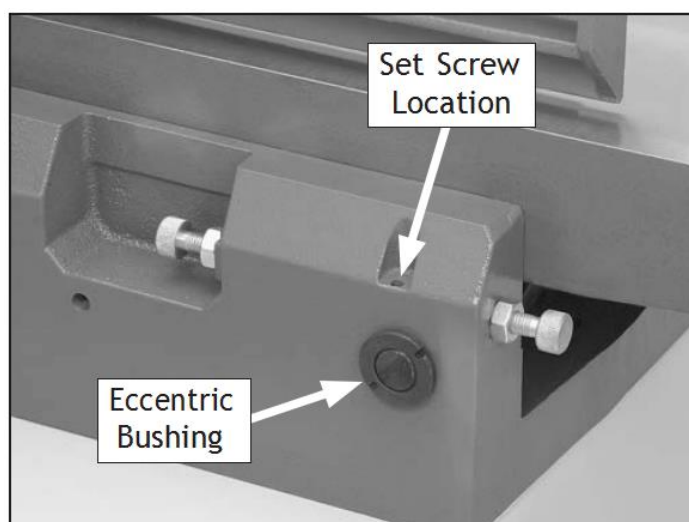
Расположение эксцентриковой втулки и установочного винта.
